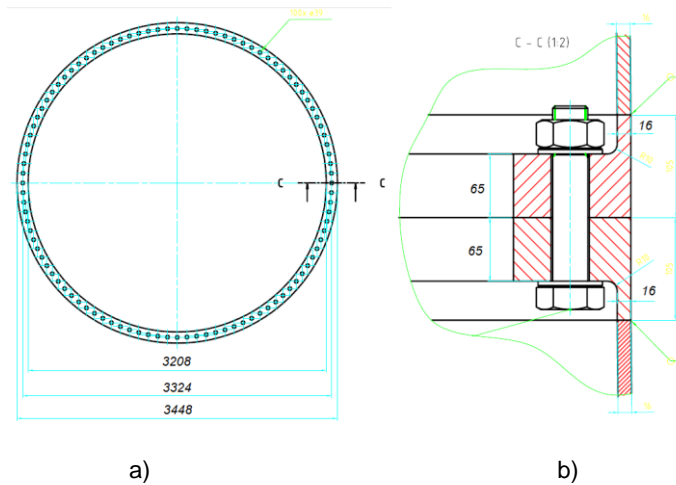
a) Esquema de uma flange média; b) Corte de uma flange média [32]
